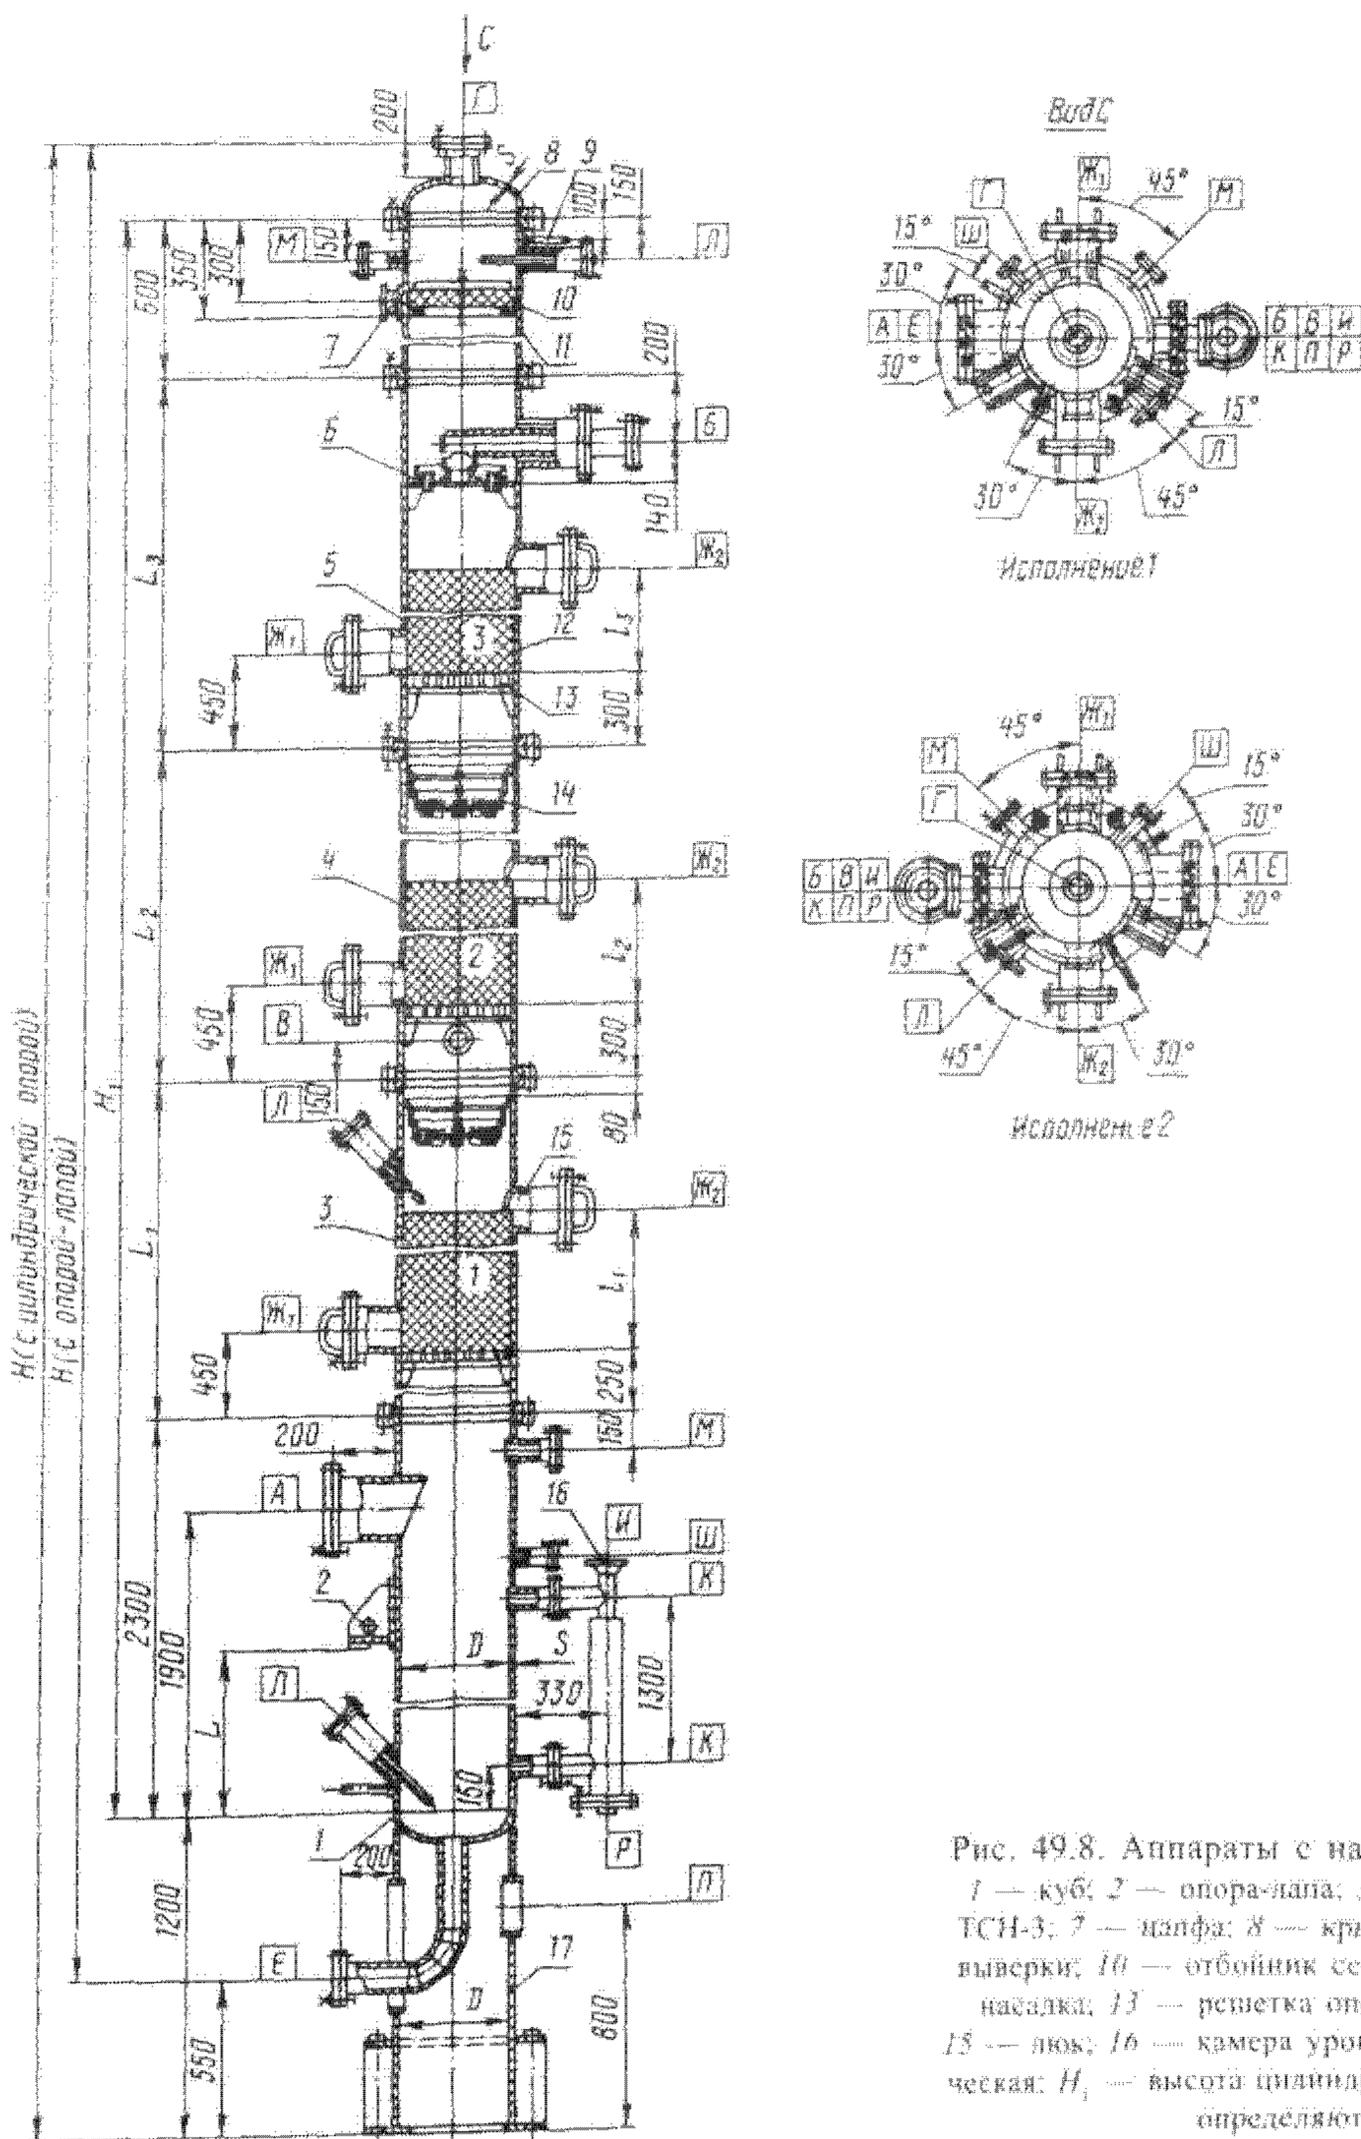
Аппараты с насыпной насадкой царговые: 1 — куб; 2 — опора-напа; 3, 4 и 5 — царги; 6 — тарелка ТСН-3; 7 — напфа; 8 — крышка; 9 — приспособление для выверки; 10 — отбойник сетчатый; 11 — сепаратор; 12 — насадка; 13 — решетка опорная; 14 — тарелка ТСН-2; 15 — люк; 16 — камера уровнемера; 17 — опора цилиндрическая;  $H_1$  — высота цилиндрической части аппарата и  $L$  — определяются заказчиком
